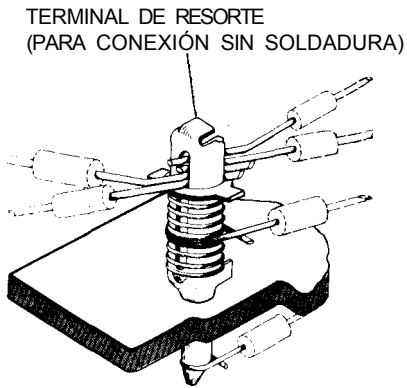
Terminal de resorte para conexión sin soldadura (Vector Electronic Company Inc.).
